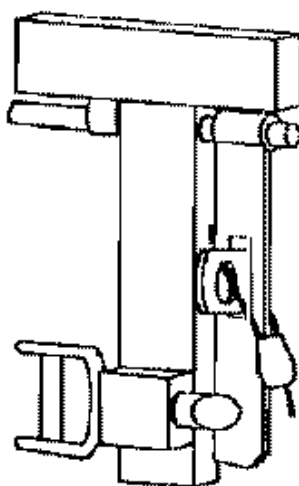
Схема установки универсального ЗПУ с длиной каната 300 мм на узле переездной площадки крытого вагона для перевозки автомобилей
